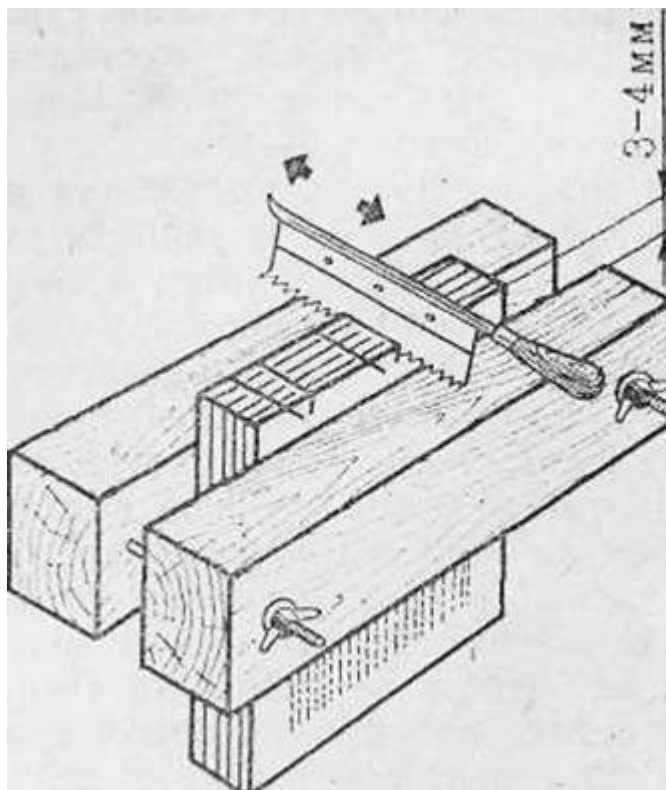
Подготовка блока с бесшвейным креплением корешка к переплету
